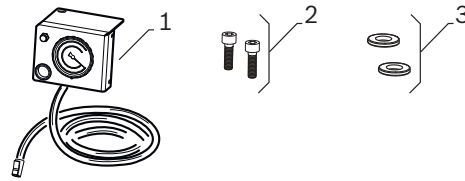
Werkzeuge zur Montage des Manometers für Reifenbefüllung
